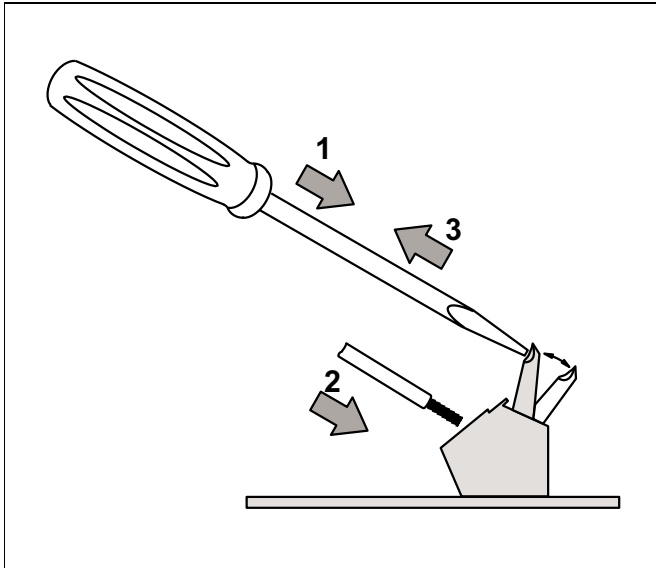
Einführung der Kabel mit schraubenlosen Federklemmen
